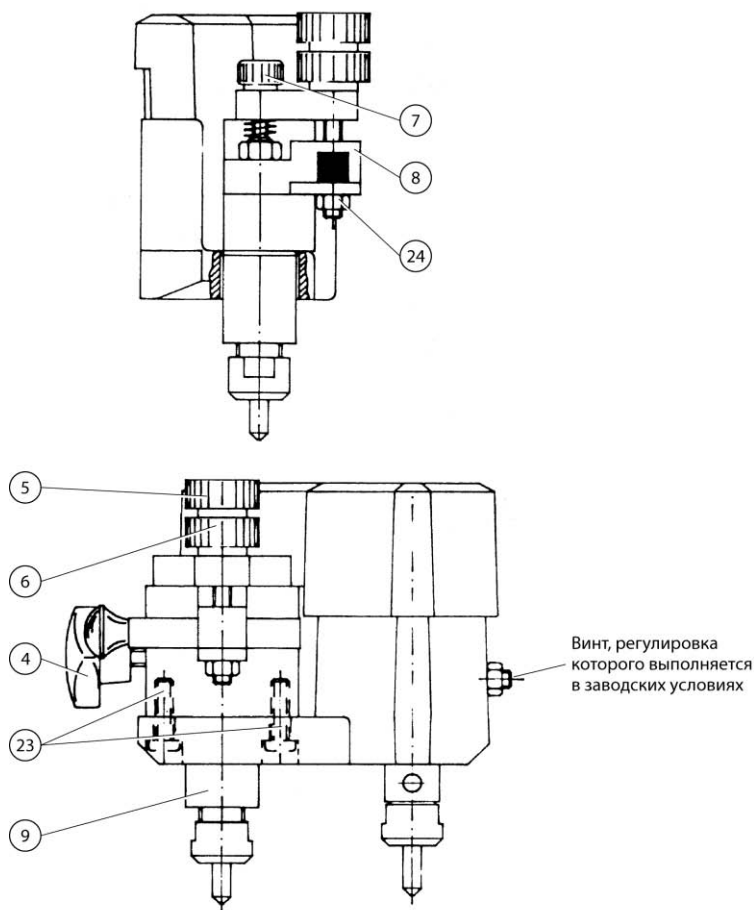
Элементы настройки станка Borkey 989 Top-Cut
